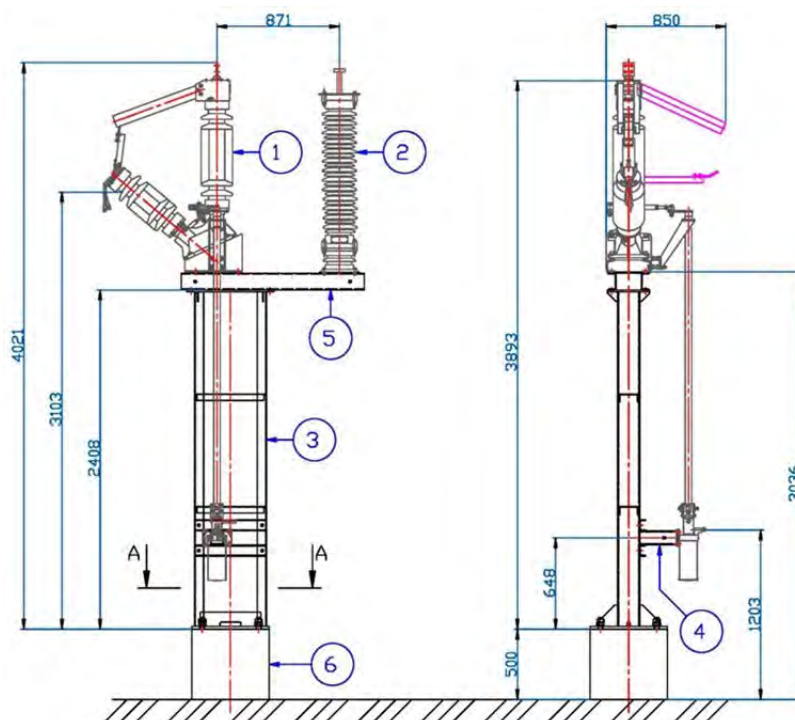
Внешний вид и габаритные размеры заземлителя
